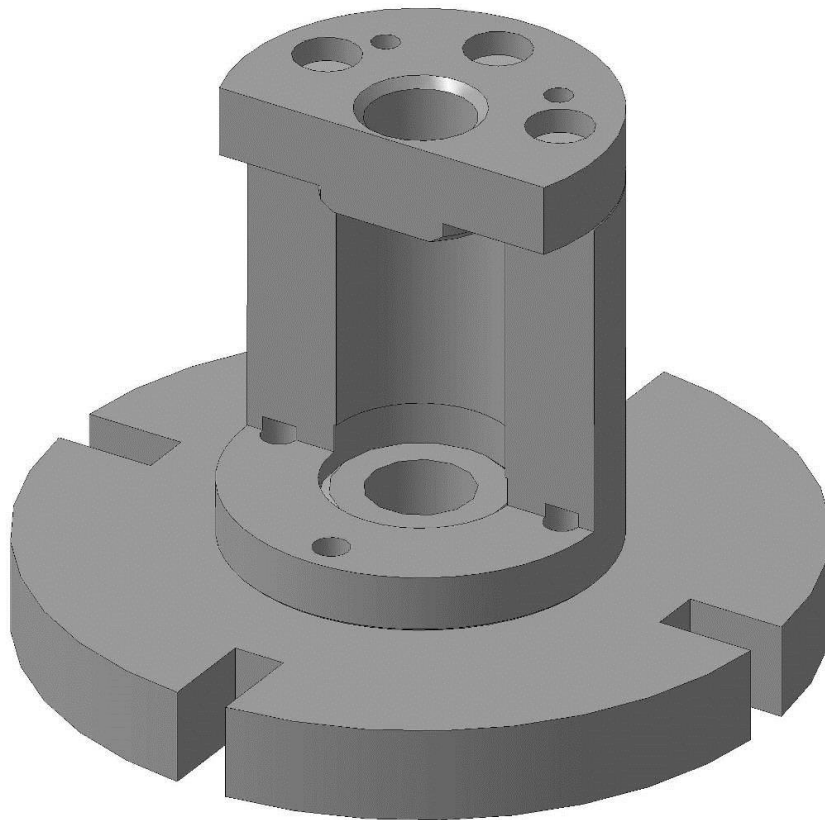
Збірне установочне пристосування для обробки робочої порожнини гальмового циліндра
